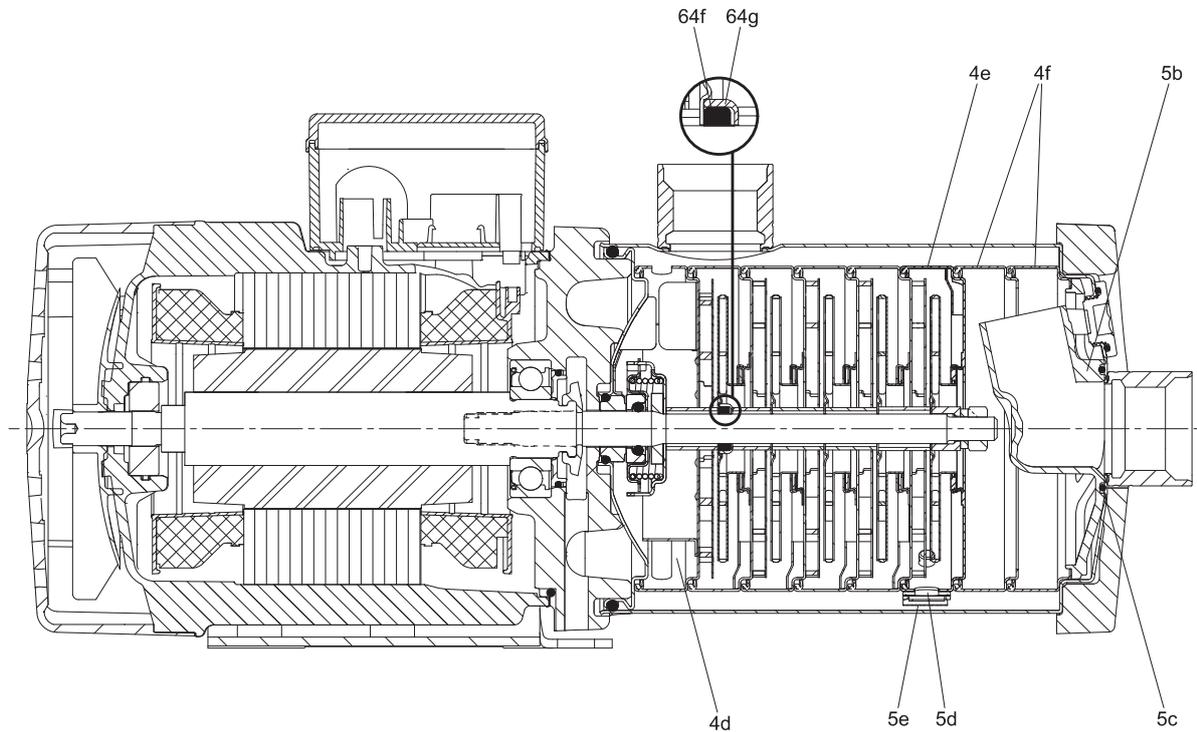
CM(E) 1-3 mit Motor MG(E) 71Bauteile
